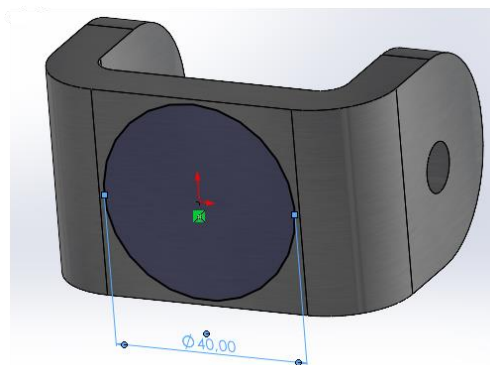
Croquis árbol de transmisión deslizante de la junta cardán en SolidWorks.
